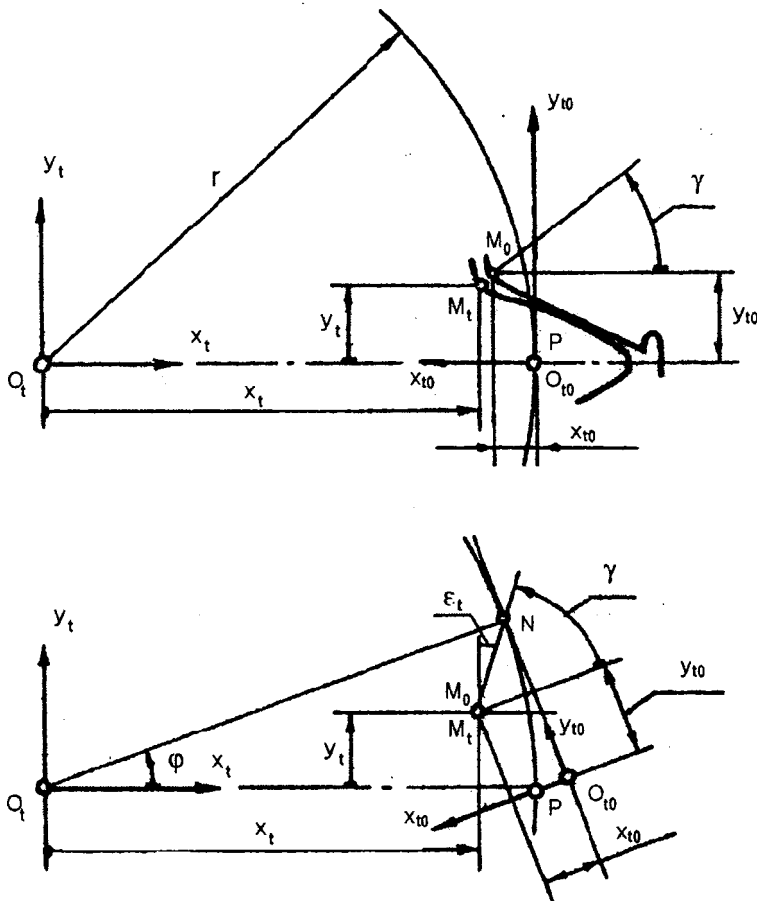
Торцовые профили производящей рейки и обрабатываемого ею зуба цилиндрического колеса.
